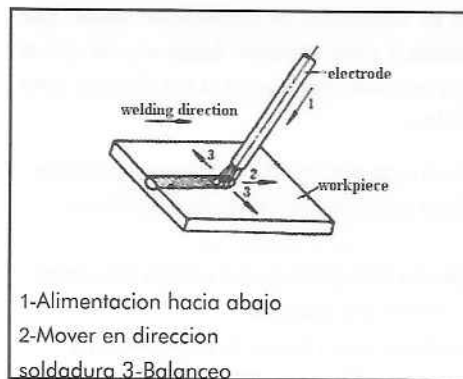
Tres direcciones básicas movimiento electrodo en soldadura plana
